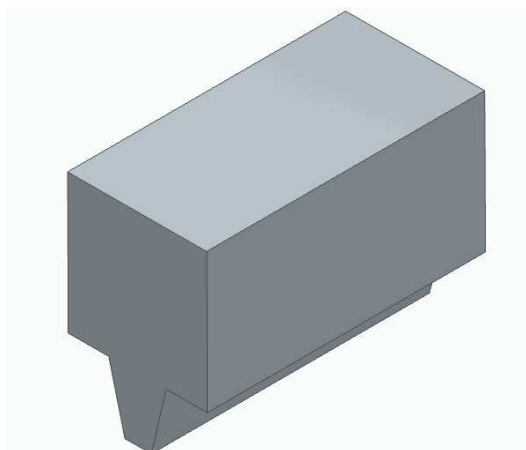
CAD del pezzo per il bloccaggio del pignone
